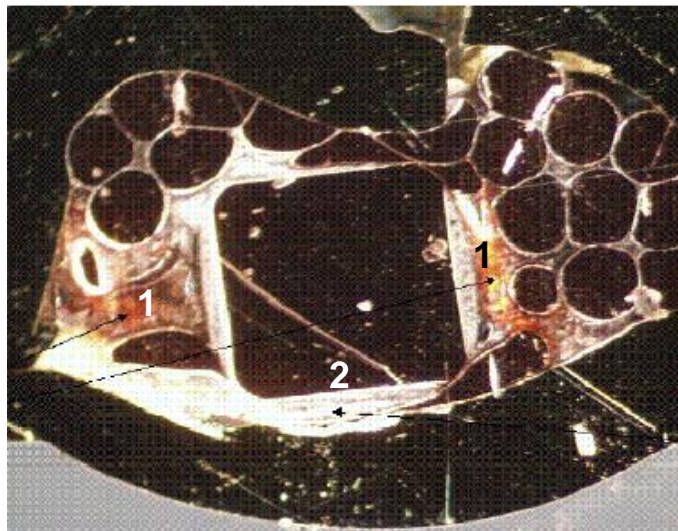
Fotomicrografía de la muestra C1 - A (proceso actual) (las flechas 1 indican el aislante derretido y la flecha 2 indica la soldadura).
